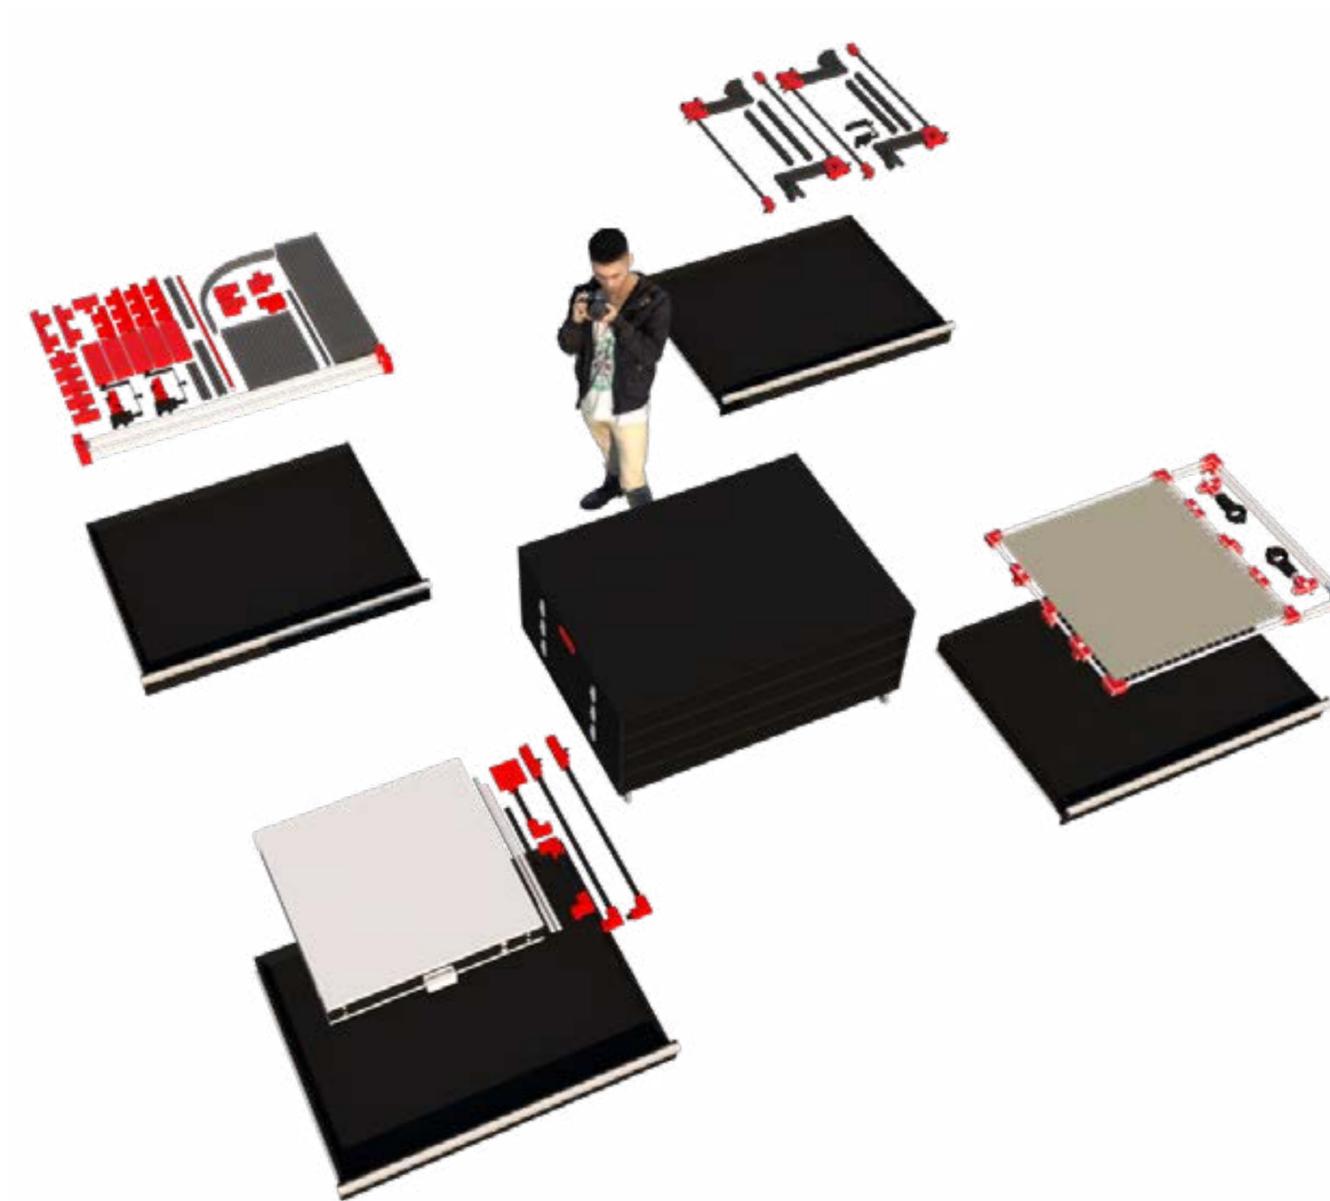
Empaque y transporte del proyecto 6 detalle piezas.
